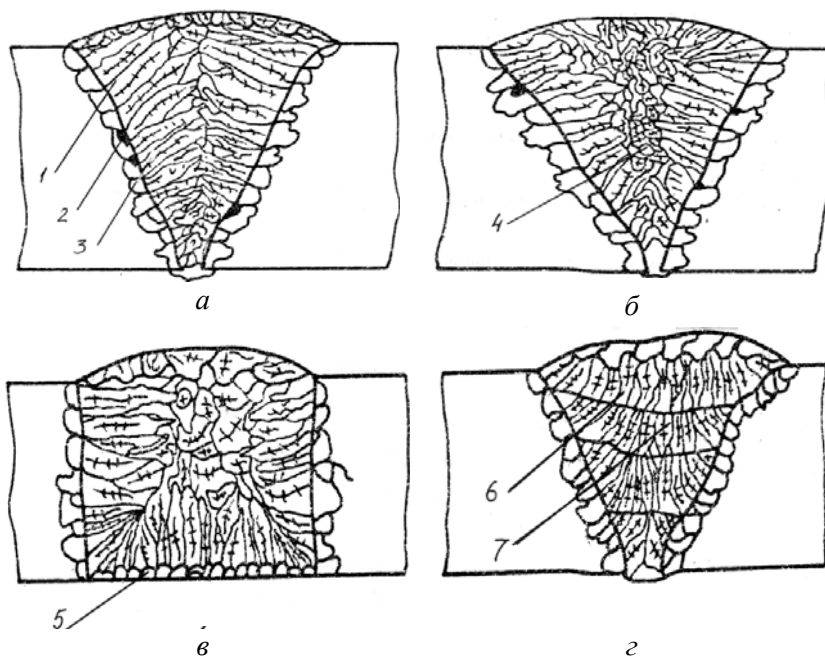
Кристаллическое строение сварного шва в поперечном сечении:
